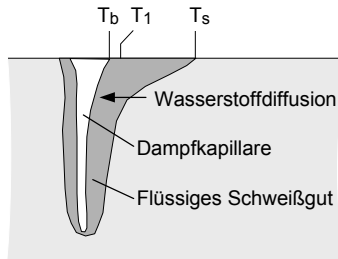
Schmelzbadentgasung beim Elektronenstrahlschweißen [93]
